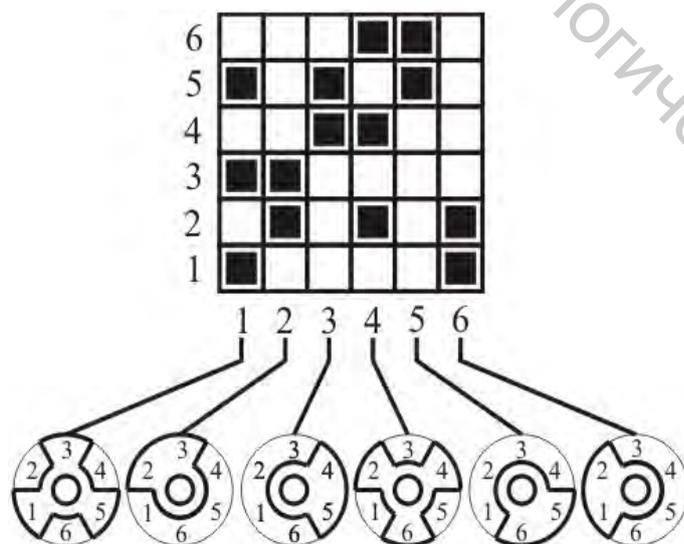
Рисунок переплетения и условные профили кулачков для кулачкового зевообразовательного механизма
